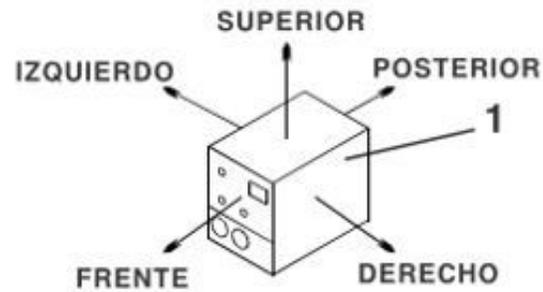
Consideración de espacios para la ubicación de la máquina soldadora.
